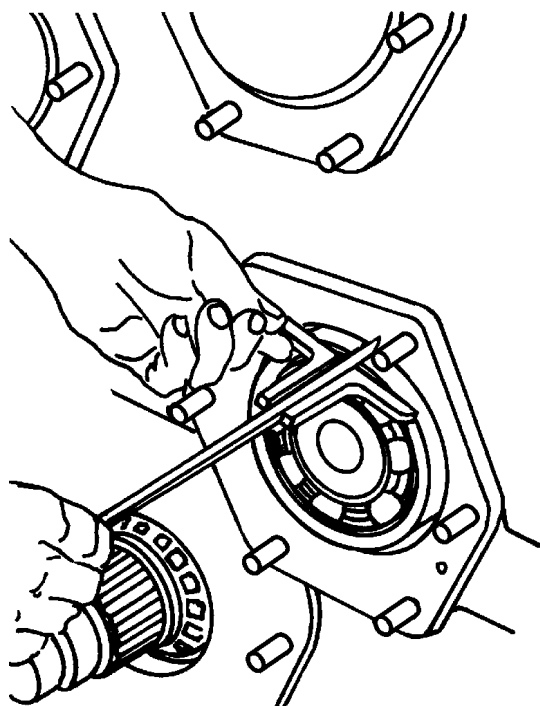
С.26. Измерение расстояния от поверхности наружной обоймы подшипника (18) до корпуса коробки передач
